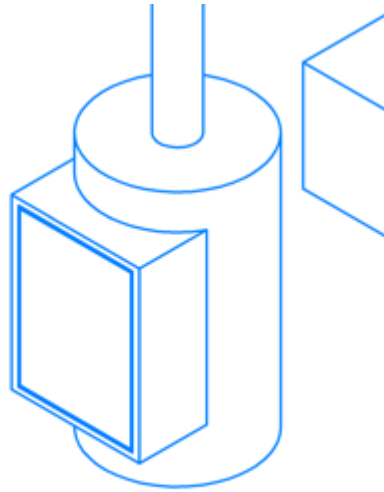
Реалізація монтування корпусу-щитка на нерухомій частині манулятора
